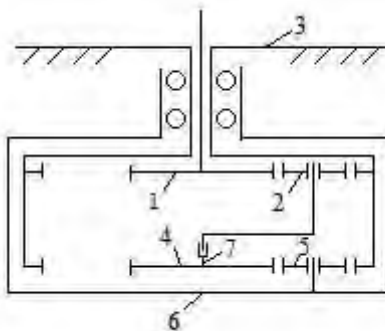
Кинематическая схема двухступенчатого планетарного редуктора:
